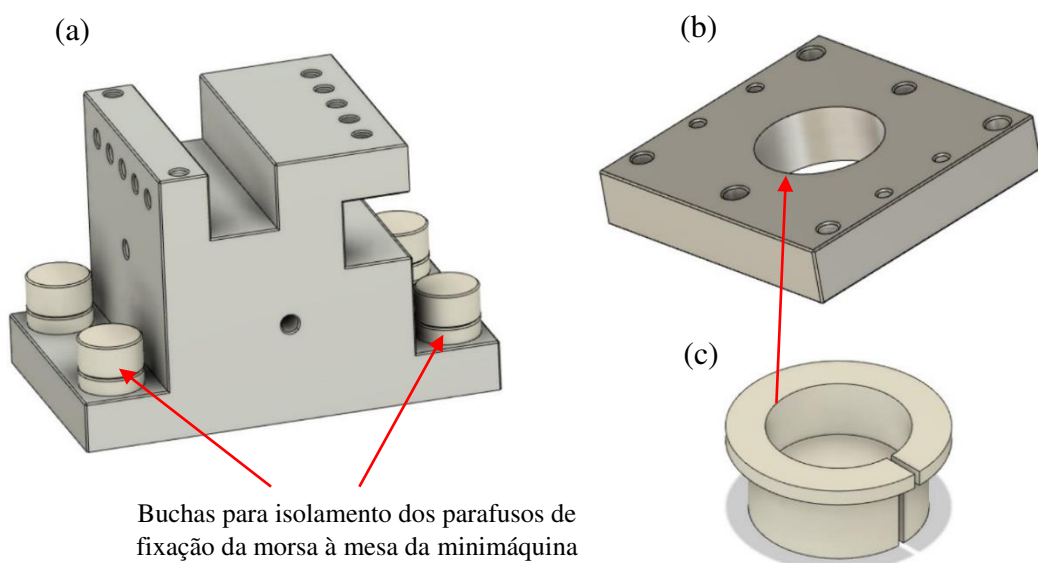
Vistas em perspectiva isométrica da (a) morsa mecânica, (b) base metálica e (c) bucha de Tecnil[®] projetadas e fabricadas para os ensaios de usinagem.
